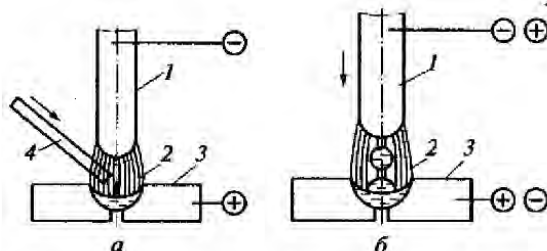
Схемы электродуговой сварки плавящимся (а) и неплавящимся (б) электродом:
